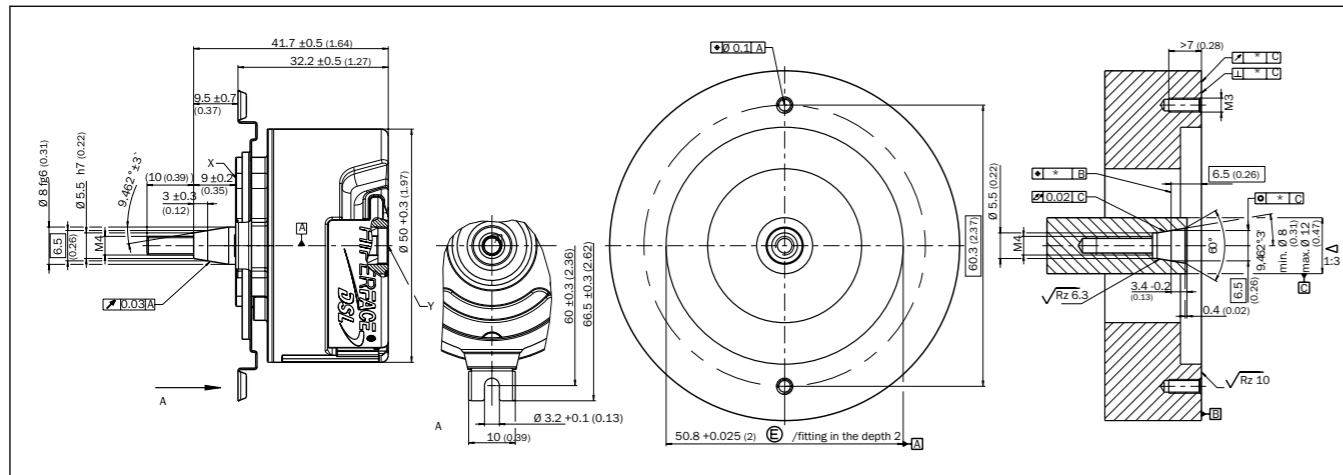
Dibujo acotado y especificación de montaje del eje cónico con acoplamiento del estator mediante chapa de resorte
